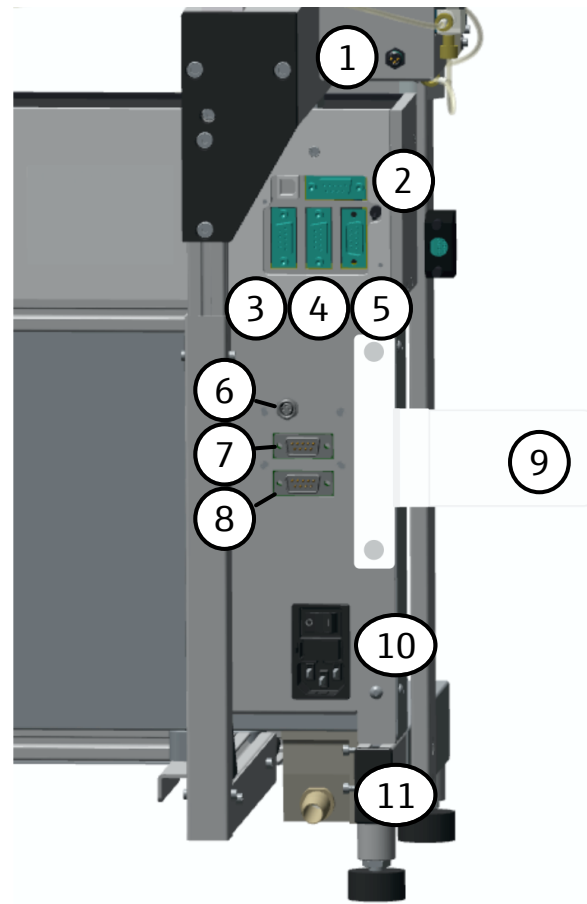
Raccords et interfaces sur la face arrière de l'appareil
